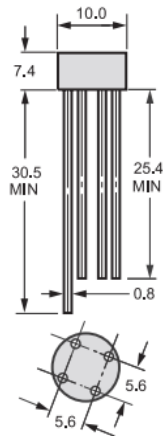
Габаритні розміри діодної зборки типу DB102
